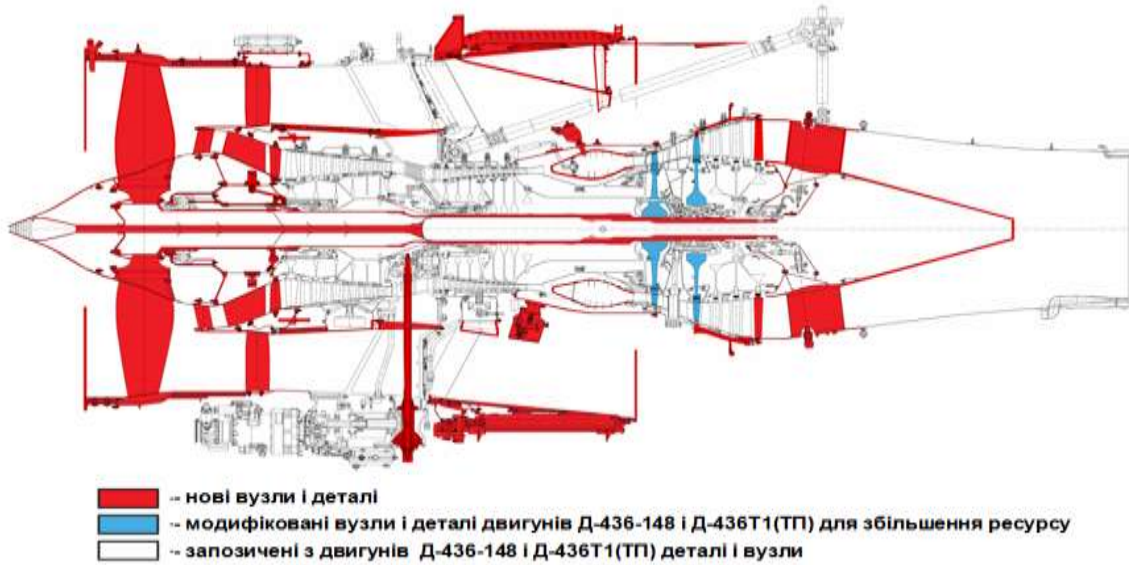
Двоконтурний турбореактивний двигун Д-436-148ФМ
